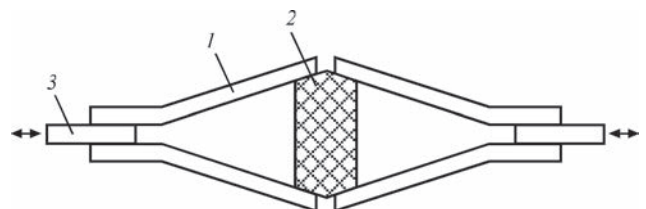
Схема составного образца для малоциклового испытания сварных соединений с угловой деформацией: 1 — испытываемые элементы; 2 — демпфер; 3 — элемент для закрепления в пульсаторе
